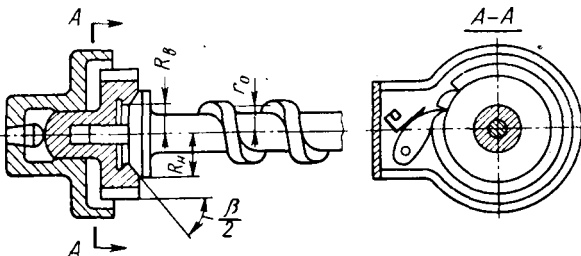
Конический грузоупорный тормоз с червячной передачей
